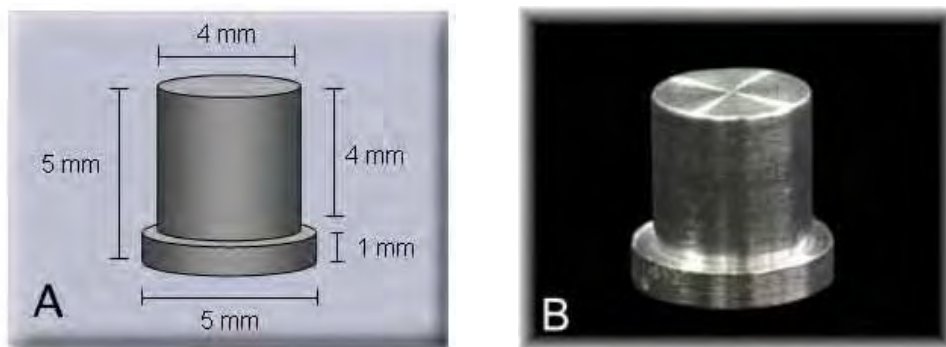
Estrutura metálica: a) esquema com as dimensões; b) estrutura metálica usinada.
